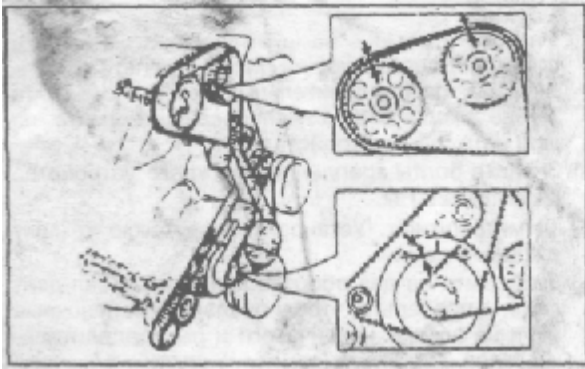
Совмещение установочных меток — Двигатель В234F
